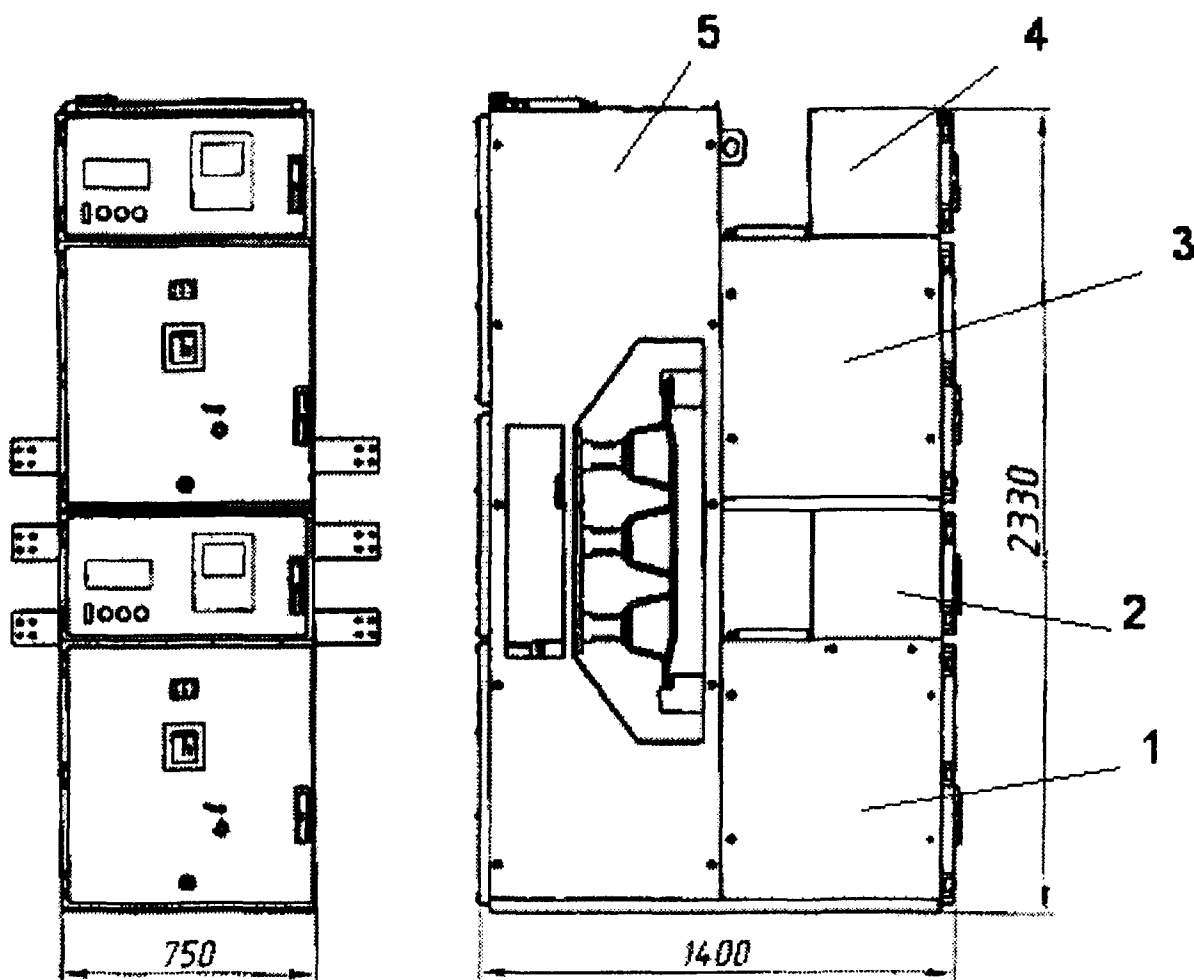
Общий вид и габаритные размеры шкафа К-125
